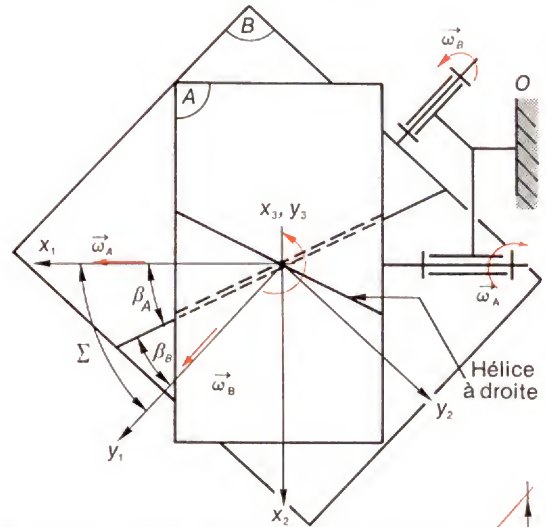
Vue de dessus de 2 roues en prise.
